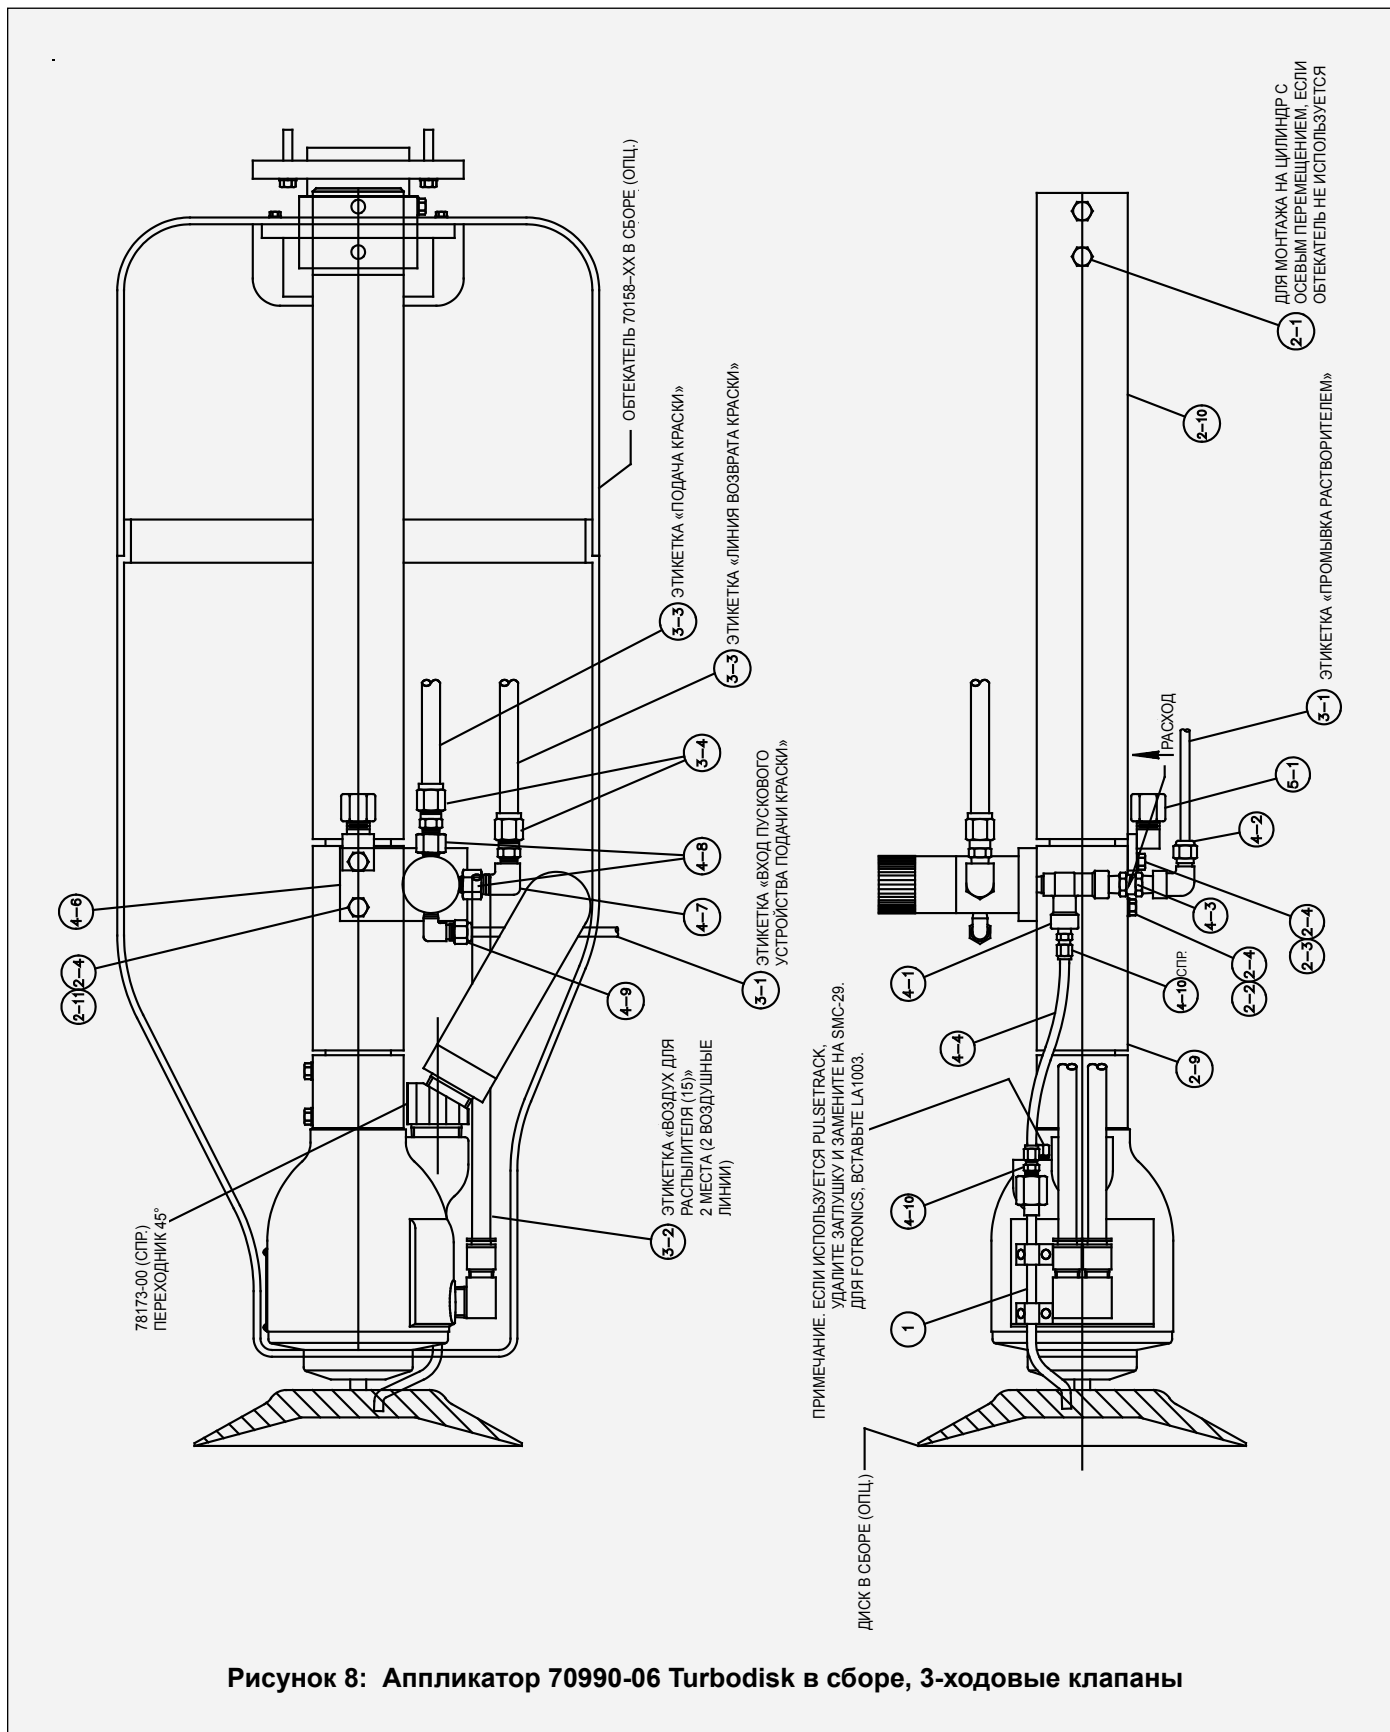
Аппликатор 70990-06 Turbodisk в сборе, 3-ходовые клапаны
